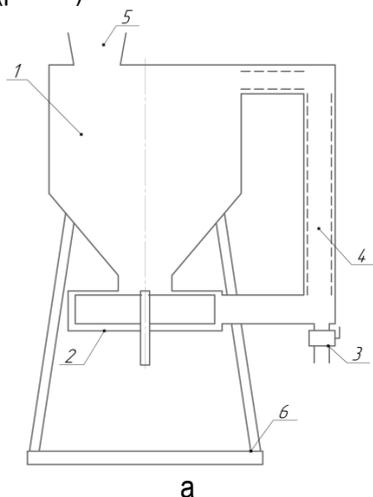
Установка для приготовления зерновой патоки с трубчатым измельчителем:
